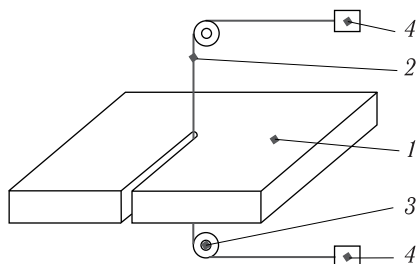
Схема электроэрозионной проволоочной резки образцов: 1 — обрабатываемая заготовка; 2 — проволока; 3 — направляющие ролики; 4 — устройство для регулирования скорости натяжения проволоки
